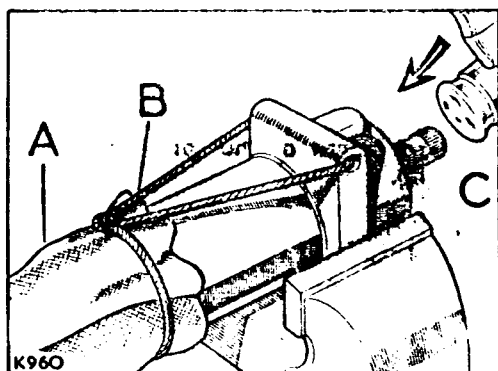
Desmontaje del eje de la caja compensadora.
